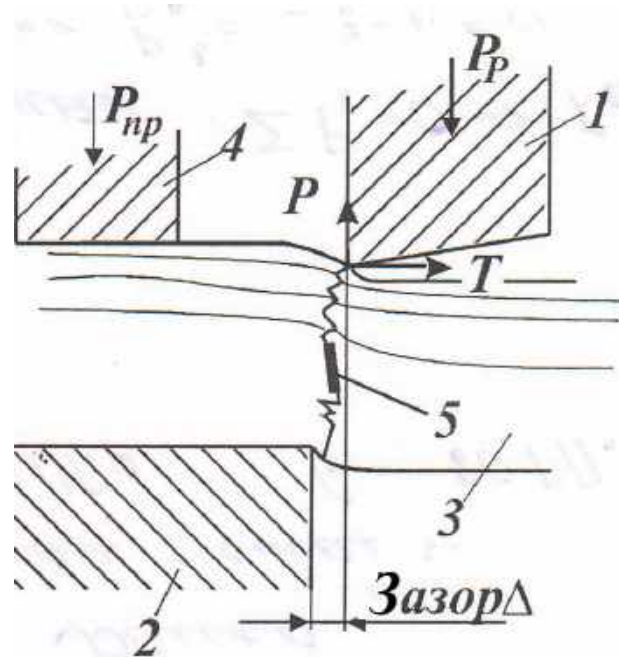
Схема різання листового металу твердим інструментом:
